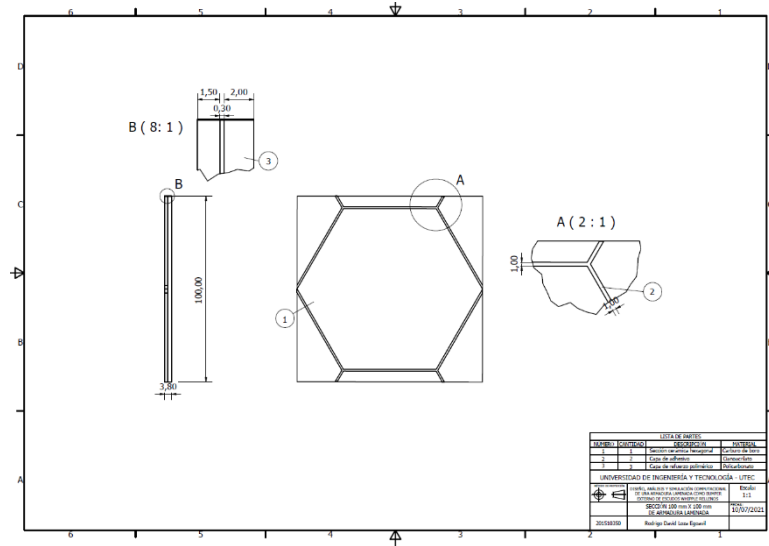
Ensamblaje general de la armadura laminada propuesta.
